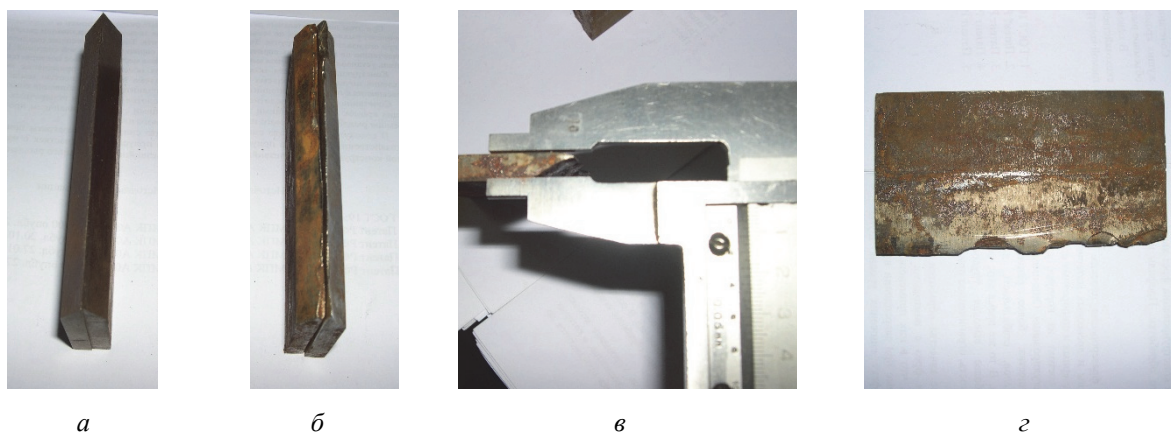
Вид разрушения рубильных ножей из биметаллических заготовок (сталь 35 и 9ХФ):
